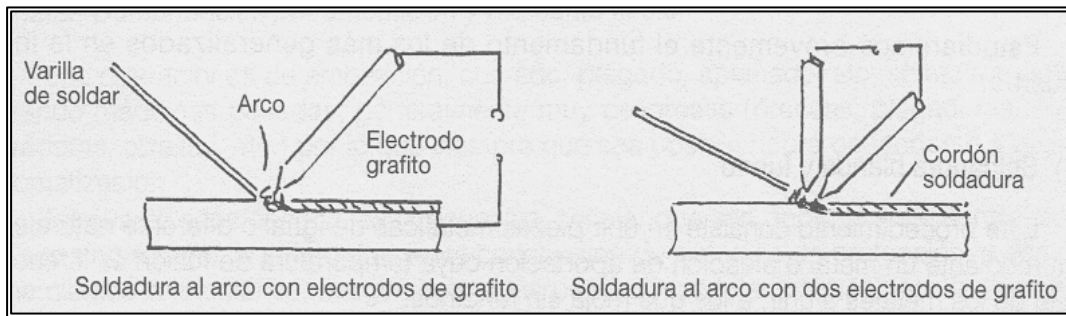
Soldadura al arco con electrodo de grafito
